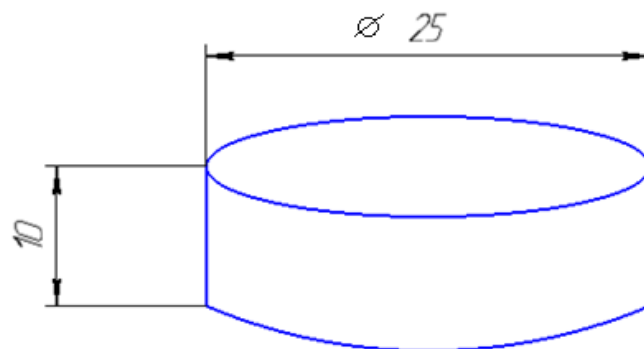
Креслення циліндричного зразка для досліджень
